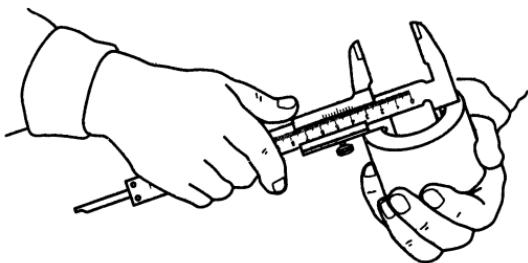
Использование штангенциркуля для измерения внутреннего размера детали
